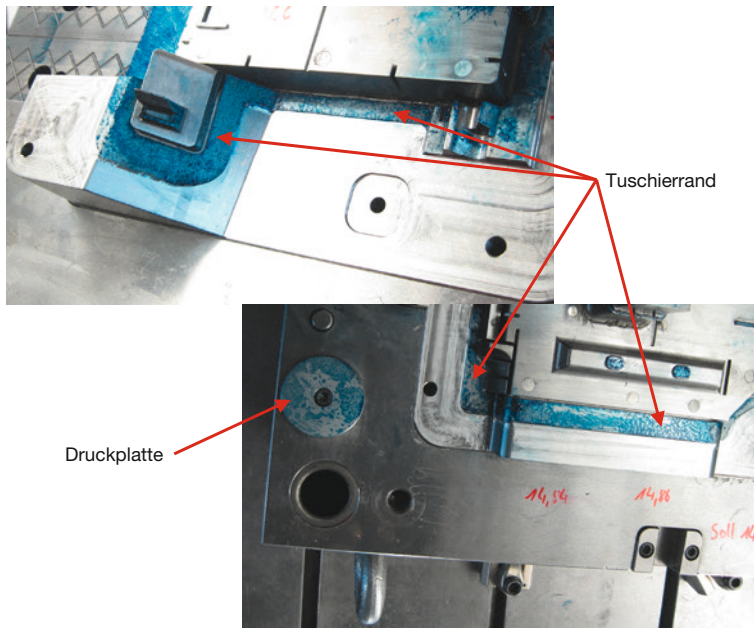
Fertig tuschiertes Spritzgießwerkzeug mit Druckplatte
